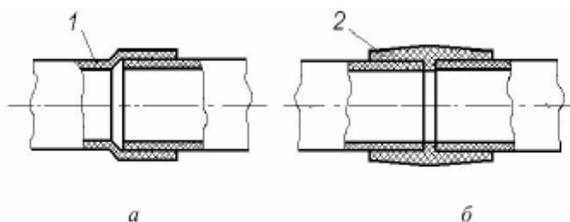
Сварные соединения труб внахлест: а – сварка с формированием раструба на одной из труб; б – сварка труб с соединительной муфтой: 1 – труба с раструбом; 2 – муфта
